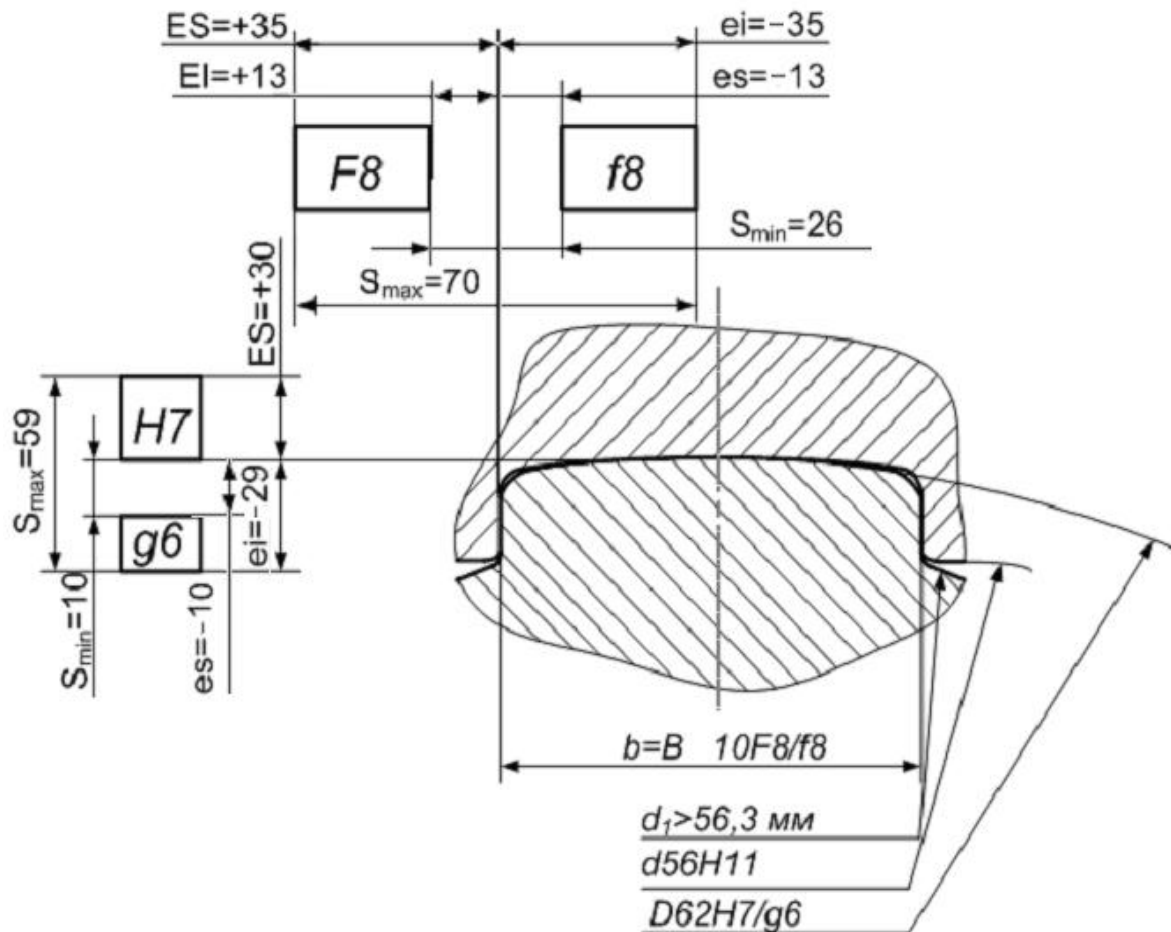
Схема розташування полів допусків шліцевого з'єднання
